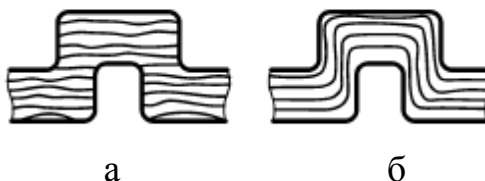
Структура коленчатого вала, изготовленного резкой из пластины (а) и по лученного операциямиковки: гибкой или передачей (б)
